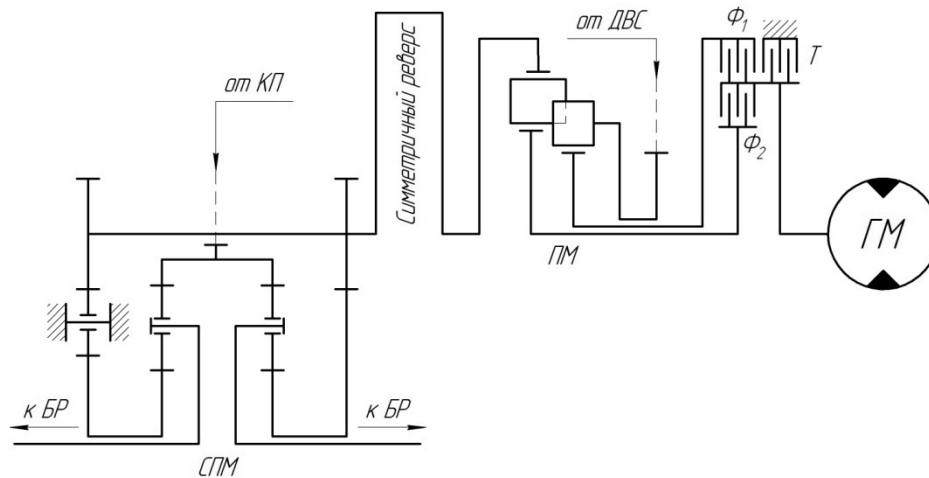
Кинематическая схема механизма передач и поворота с непрерывно-ступенчатой ГОМП: ГМ – гидромотор; ПМ – планетарный механизм двухпоточного механизма поворота; СПМ – бортовые суммирующие планетарные механизмы; БР – бортовые редукторы; Ф1, Ф2, Т – фрикционные управляемые элементы
